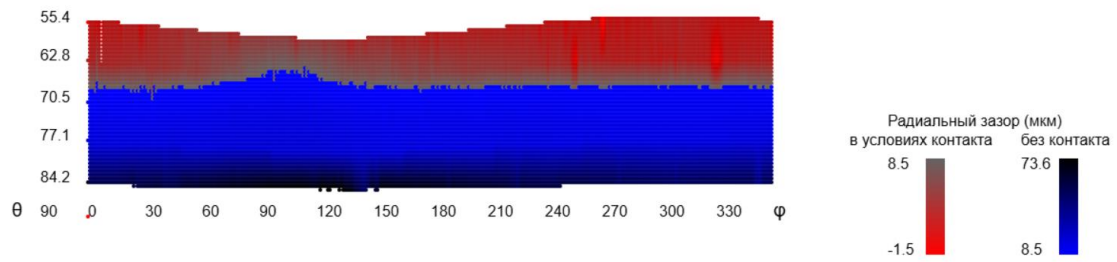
Развертка сферической поверхности крышки №3 после притирки
